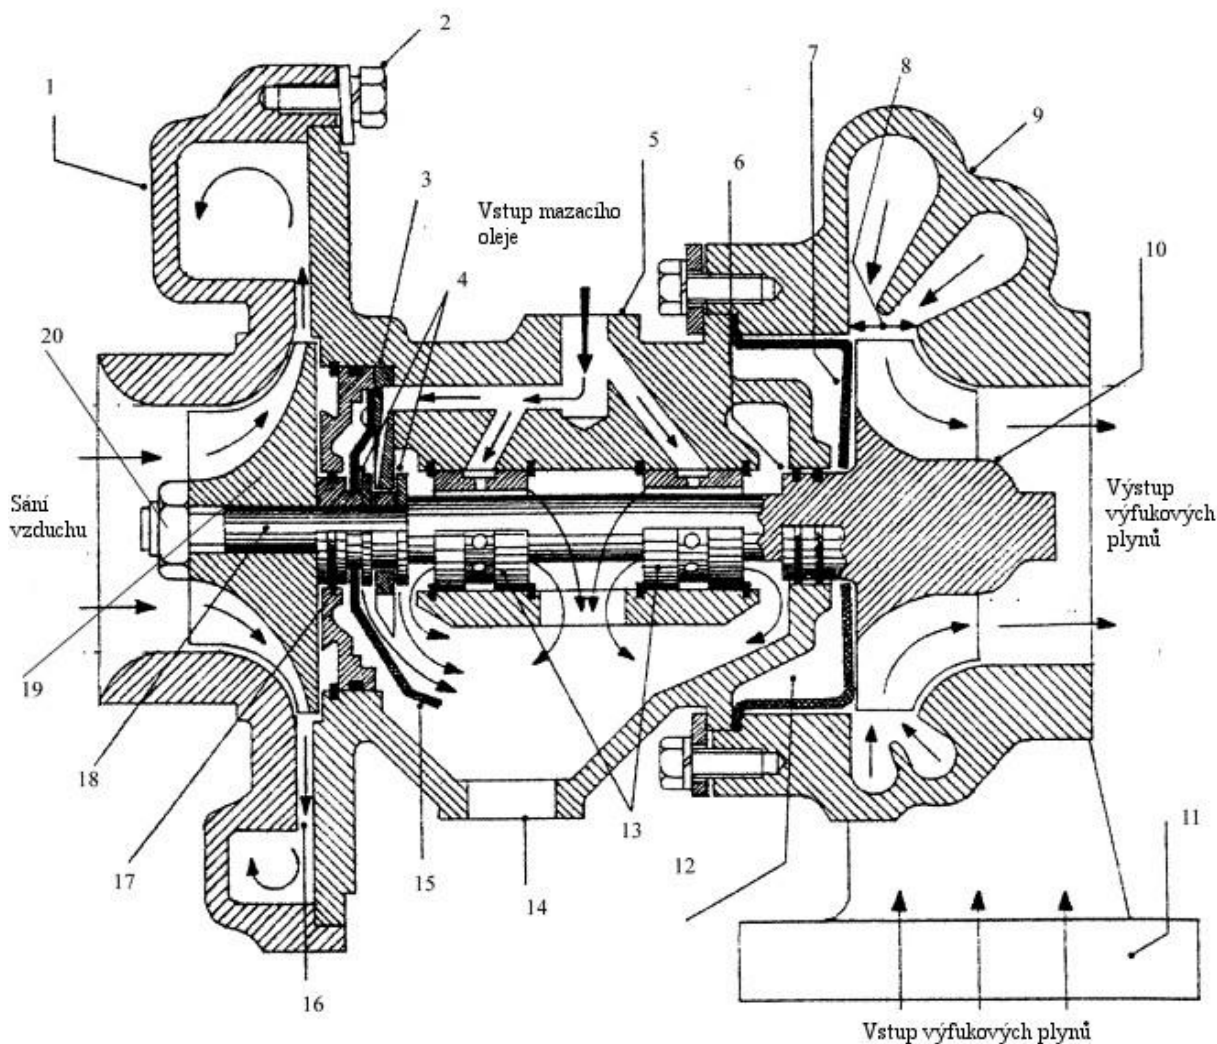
Princip přeplňování turbodmychadlem [2]
